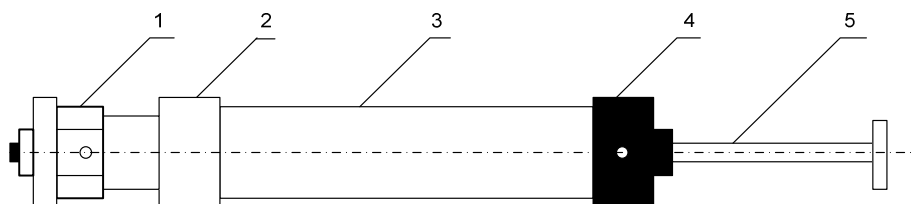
Внешний вид насоса-пробоотборника НП-3М: 1 – насадка; 2 – переходная втулка; 3 – цилиндр; 4 – крышка; 5 – шток
